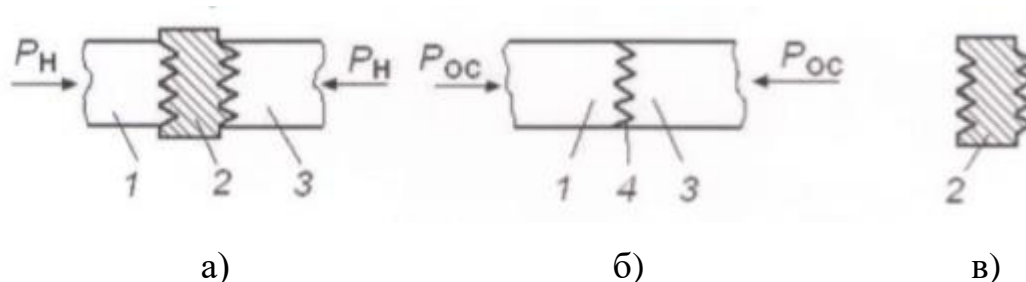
Схема сварки встык нагретым профилированным инструментом: а – нагрев кромок; б – осадка; в – инструмент; 1,3 – соединяемые детали; 2 – инструмент; 4 – шов;  $P_n$  – давление нагрева;  $P_{oc}$  – давление осадки [11]
